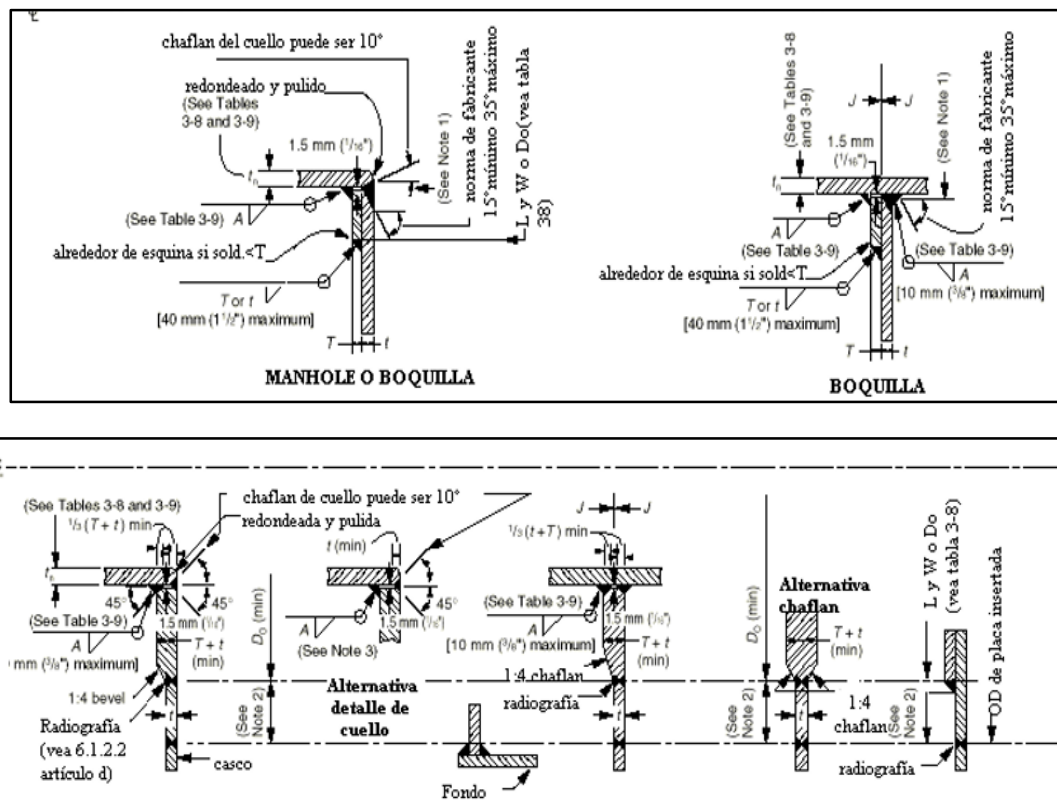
Reforzamiento tipo insertado para manholes y boquillas
